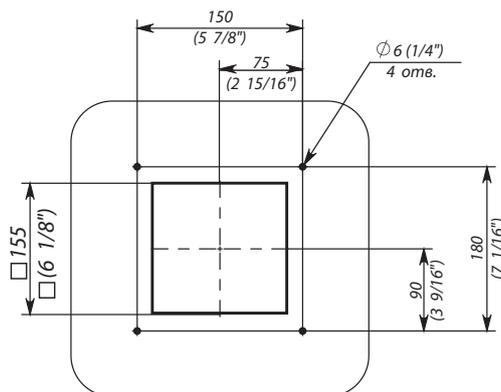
Схема разметки отверстий под крепеж блока вентилятора
